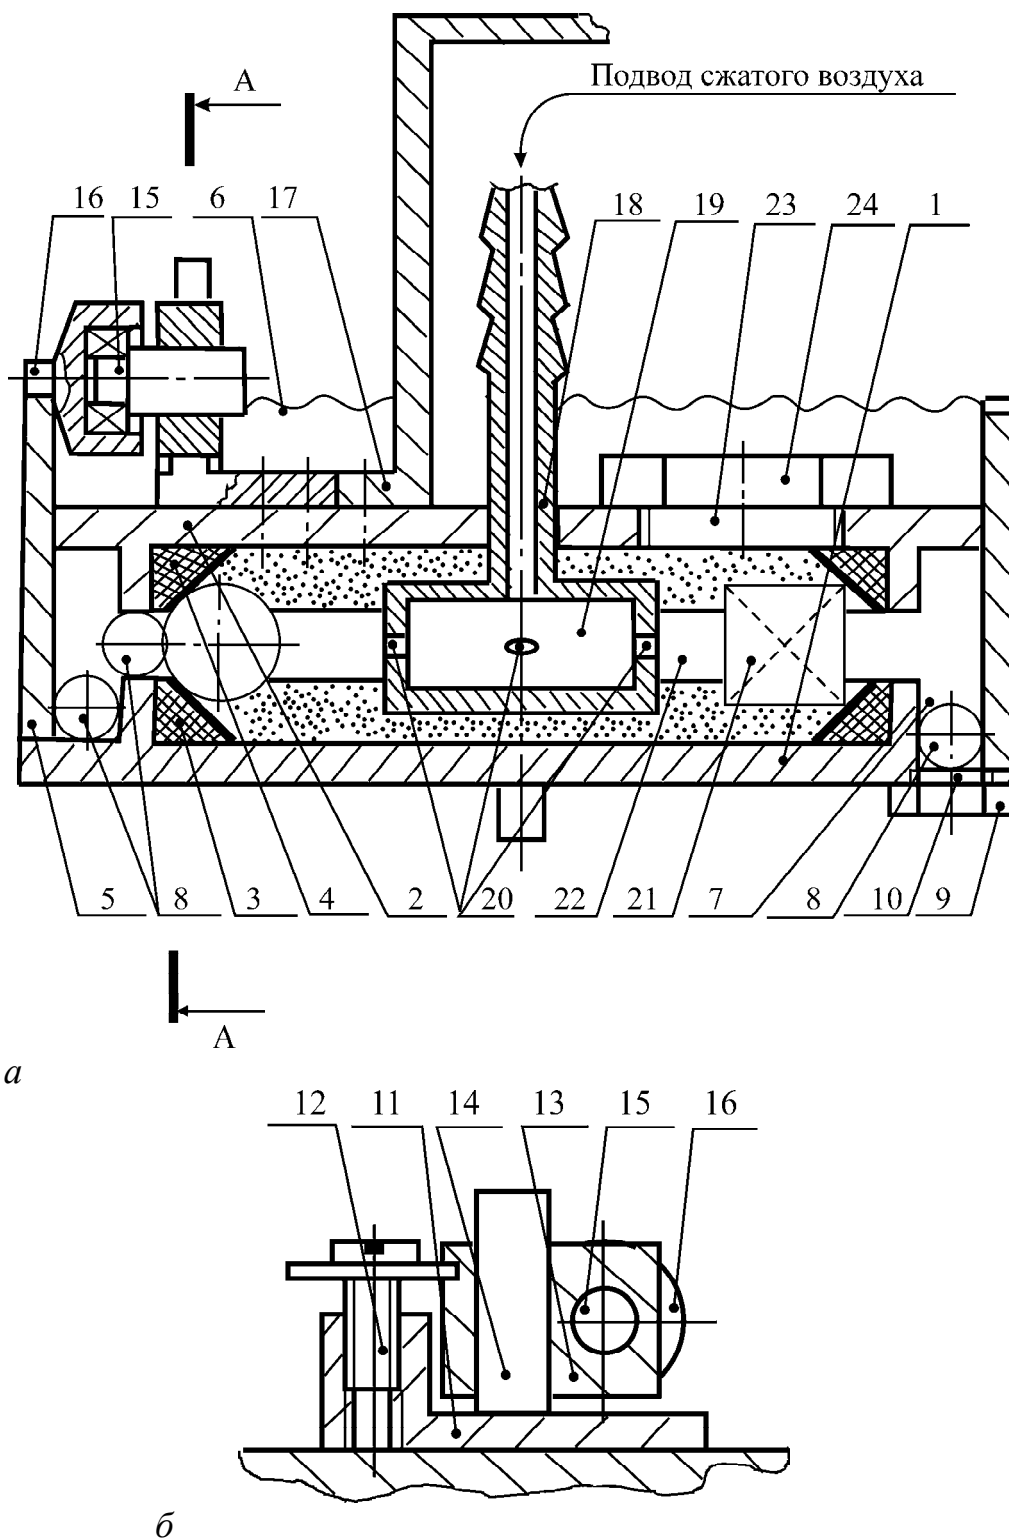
Модернизированное устройство для центробежной обработки шариков
